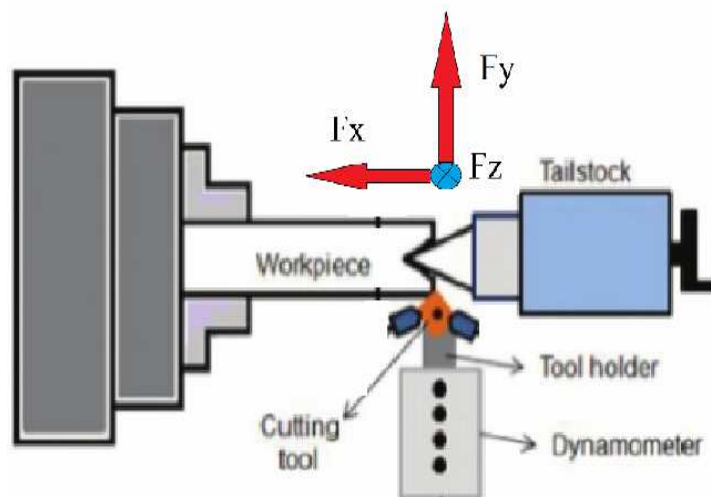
Força de usinagem e suas componentes para processo de torneamento.
